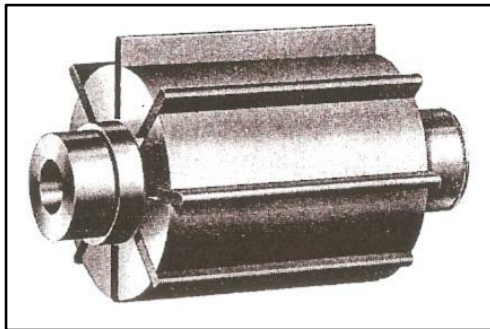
Disposição das palhetas em um rotor de compressor de palhetas deslizantes.
